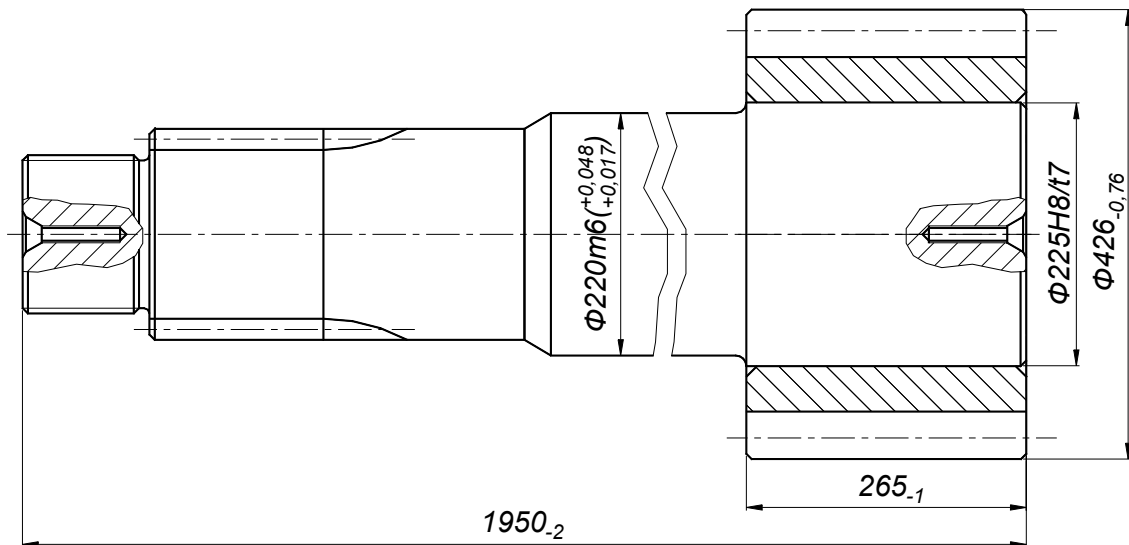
Предложенная конструкция вал шестерни экскаватора ЭКГ-8
